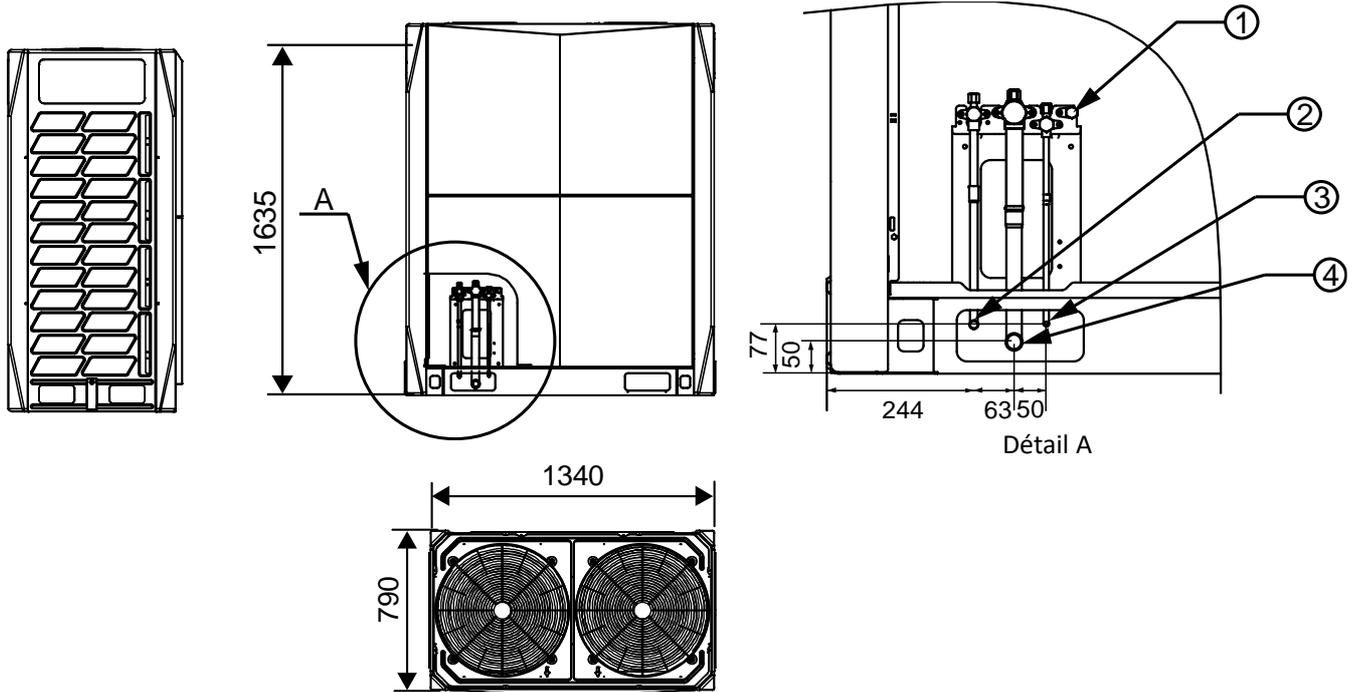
K2F-252(280, 335) DN4S dimensions (unité : mm)
